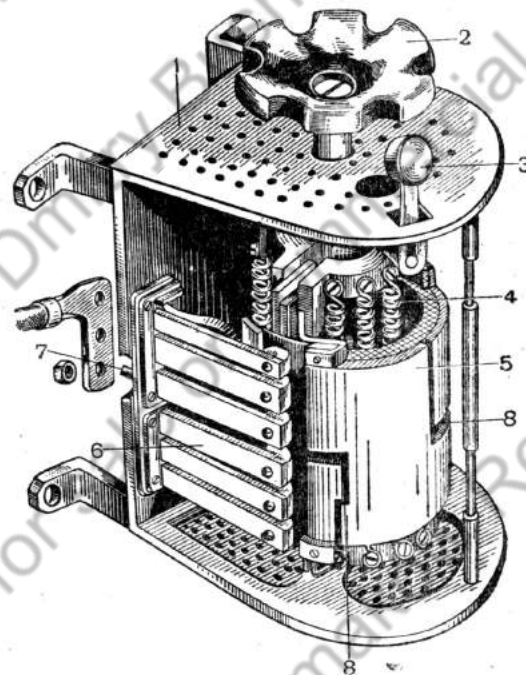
Контроллер со снятым кожухом (общий вид): 1 — основание контроллера с двумя стенками; 2 — маховичок сарабана; 3 — выноса фиксатора; 4 — сопротивленец; 5 — барабан с фидурными пластинами; 6 — щётки; 7 — винты; 8 — воздушный изоляционный промежуток
